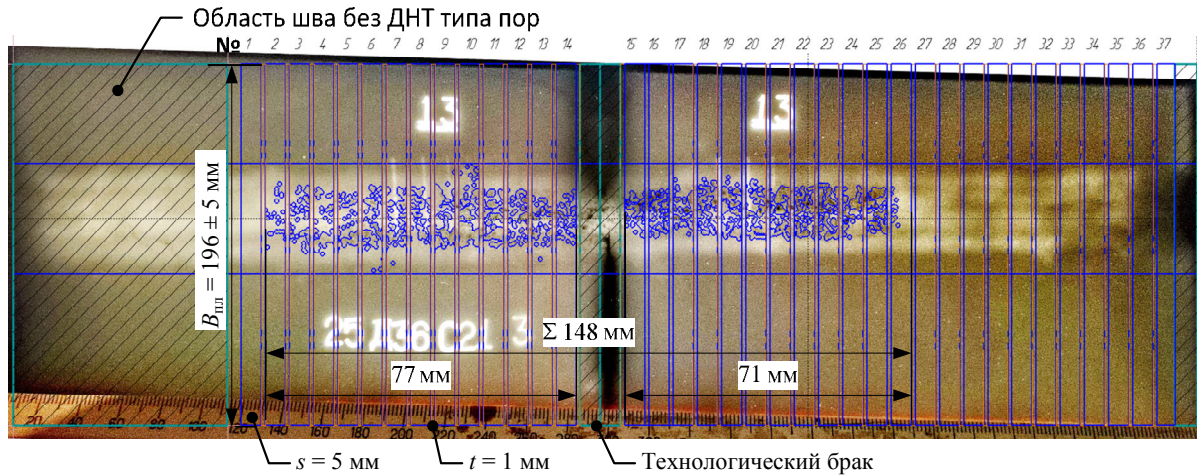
Общая схема компьютерной обработки снимка РМК с ДНТ (поры) в сварном шве пластины № 3
